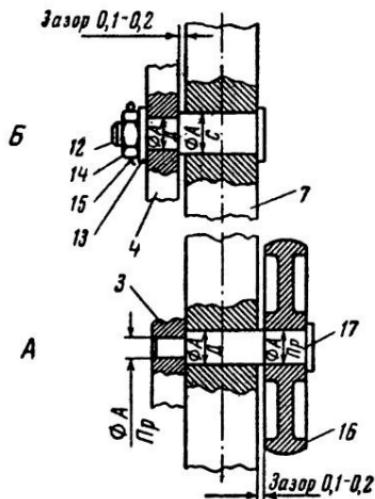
Модель плоскоременной передачи с натяжным роликом (схема соединения деталей): А — узел ведущего вала (3 — рычаг привода, 16 — ведущий шкив, 17 — ведущий вал); Б — узел крепления натяжного устройства (4 — рычаг натяжного устройства, 7 — стойка, 12 — ось натяжного устройства, 13 — шайба, 14 — гайка, 15 — сплинт).
